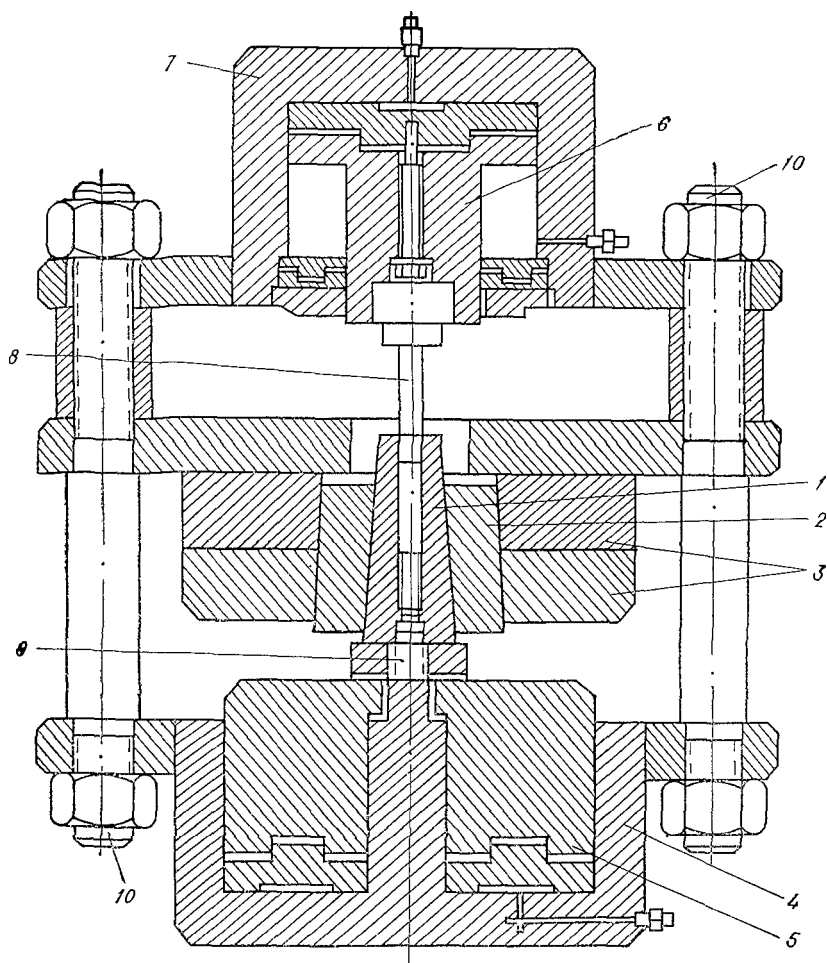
Гидростатический аппарат системы цилиндр — поршень с двойной механической поддержкой.
